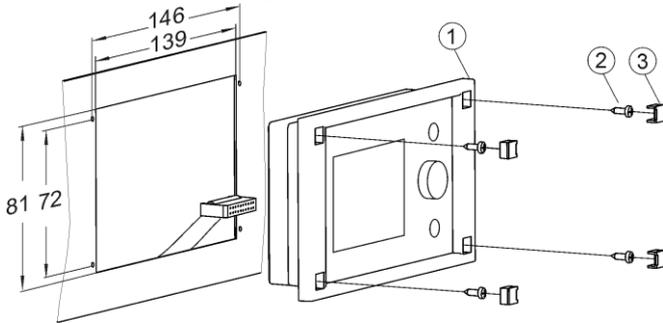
Einbau des Panels in die Montageplatte; 1 - Steuerpanel, 2 - Blechschraube 2.9x13, 3 - Blende.
